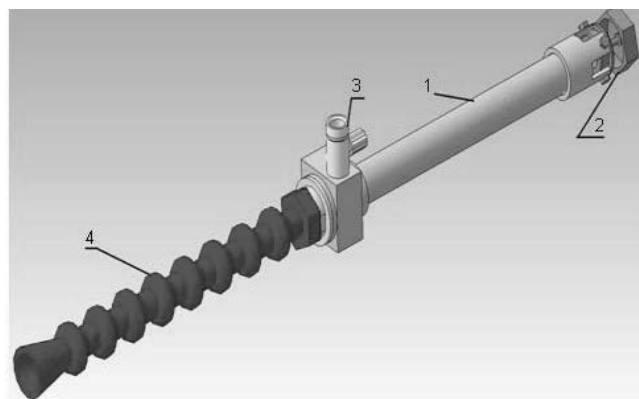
3D-модель конструкции противоточной вихревой трубы: 1 — вихревая труба; 2 — ручка; 3 — дроссель; 4 — полишарнирная трубка
